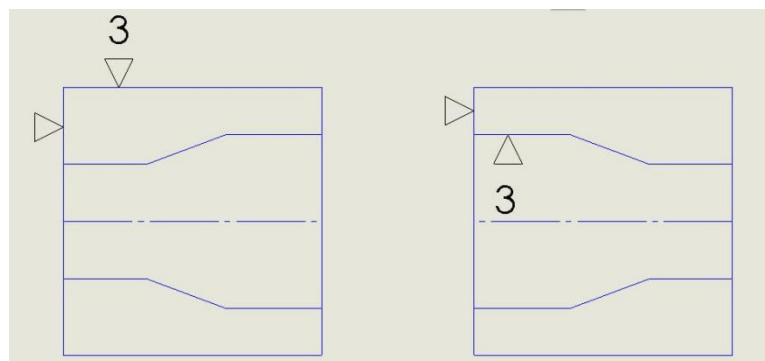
Схема базування заготовки для установи 1 та установи 2 на операцію 020
